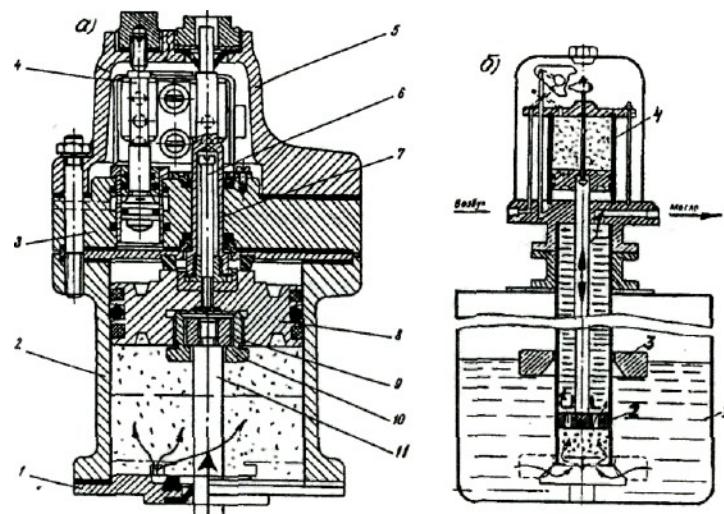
Устройство (а) и схема (б) работы пневматического двигателя
